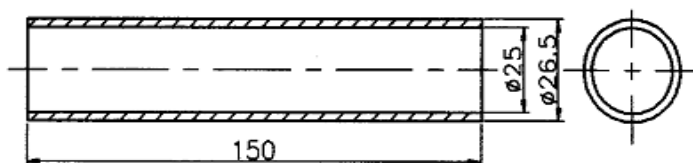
Эскиз обрабатываемой трубы из стали STS304
